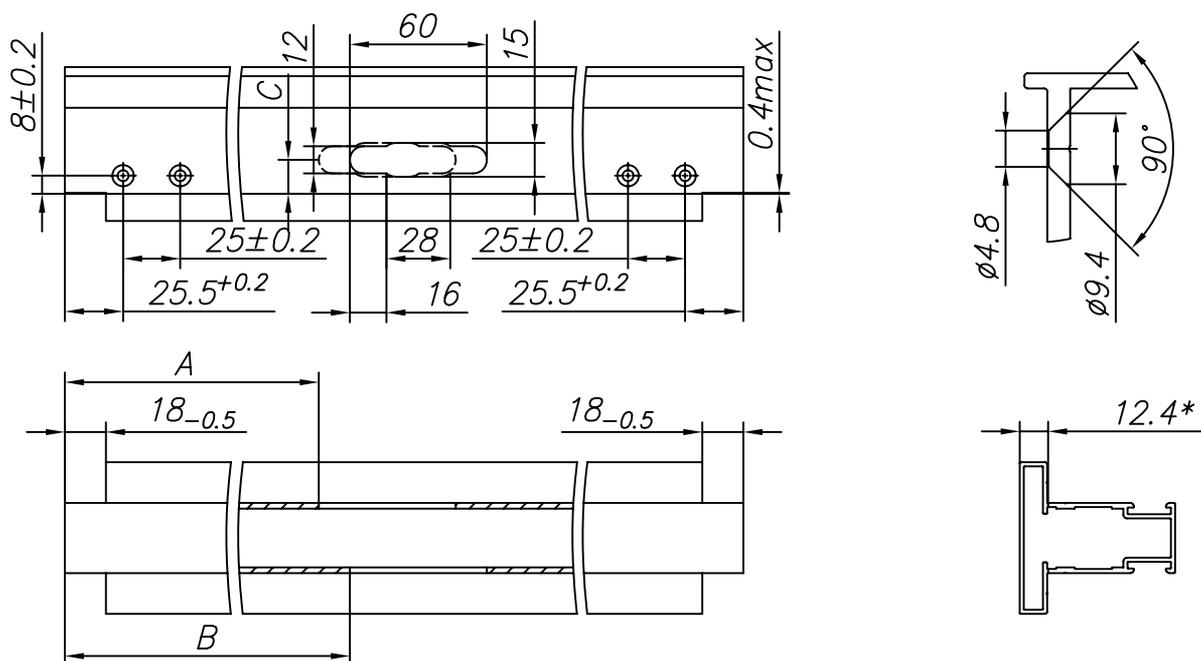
Изготовление импоста с пазами для тросовой растяжки
